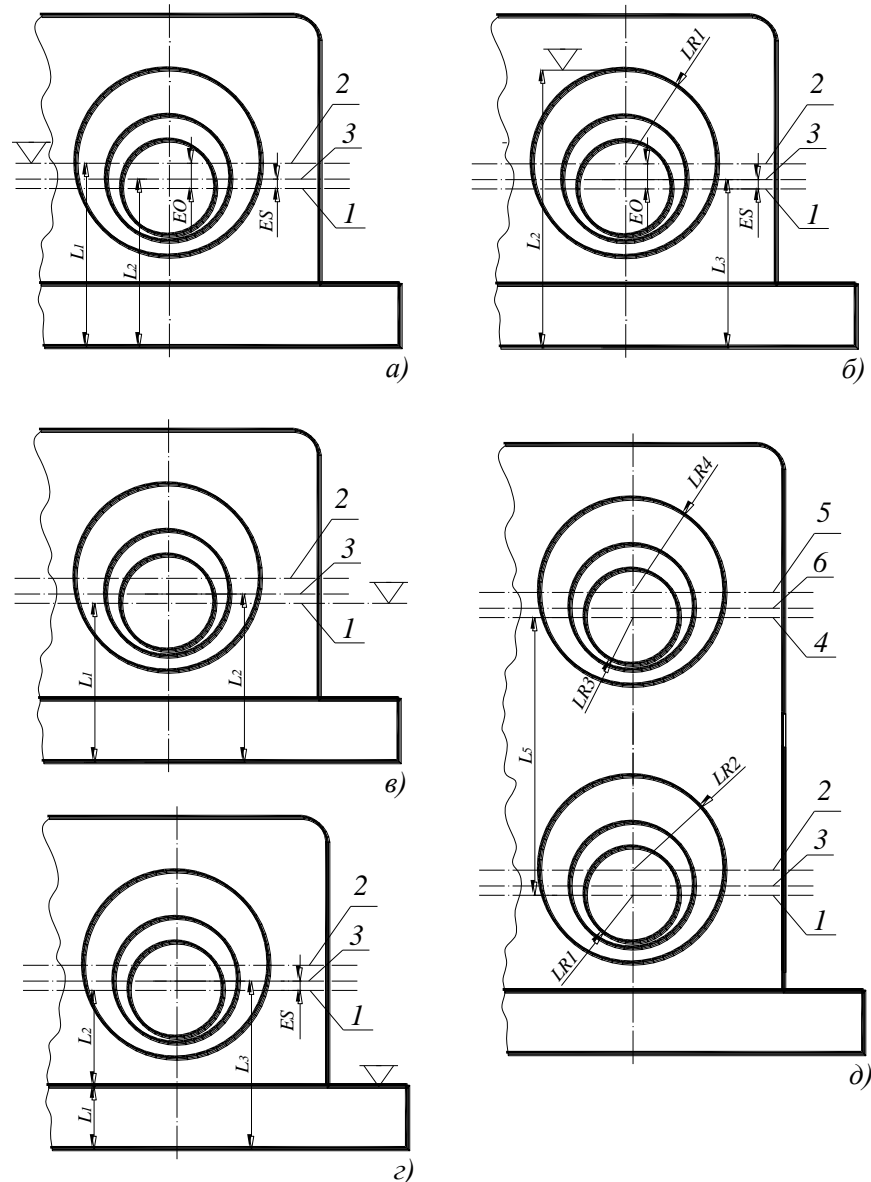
Основні варіанти базування корпусних деталей на верстатах при механічній обробці в напрямку осі координат  $OZ$
